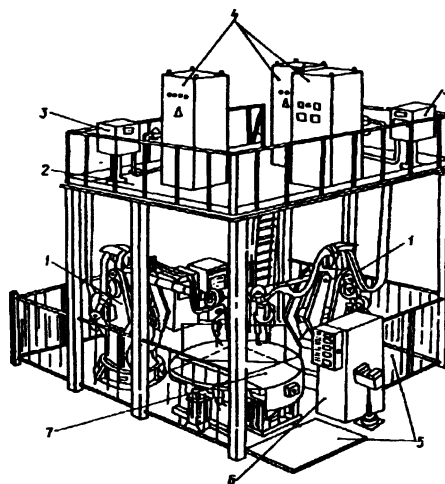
Автономный комплекс с двумя роботами для точечной сварки:
